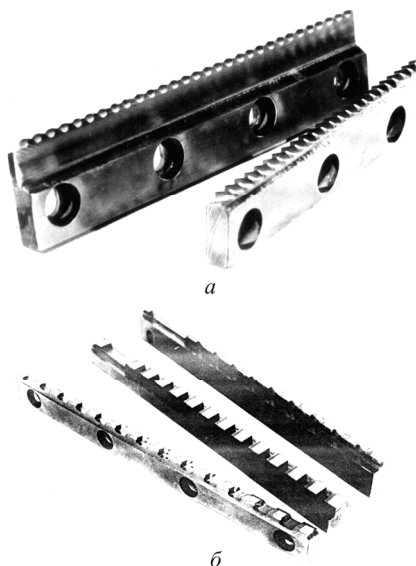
Общий вид быстрорежущих (а) и твердосплавных (б) протяжек для обработки замков лопаток компрессора
